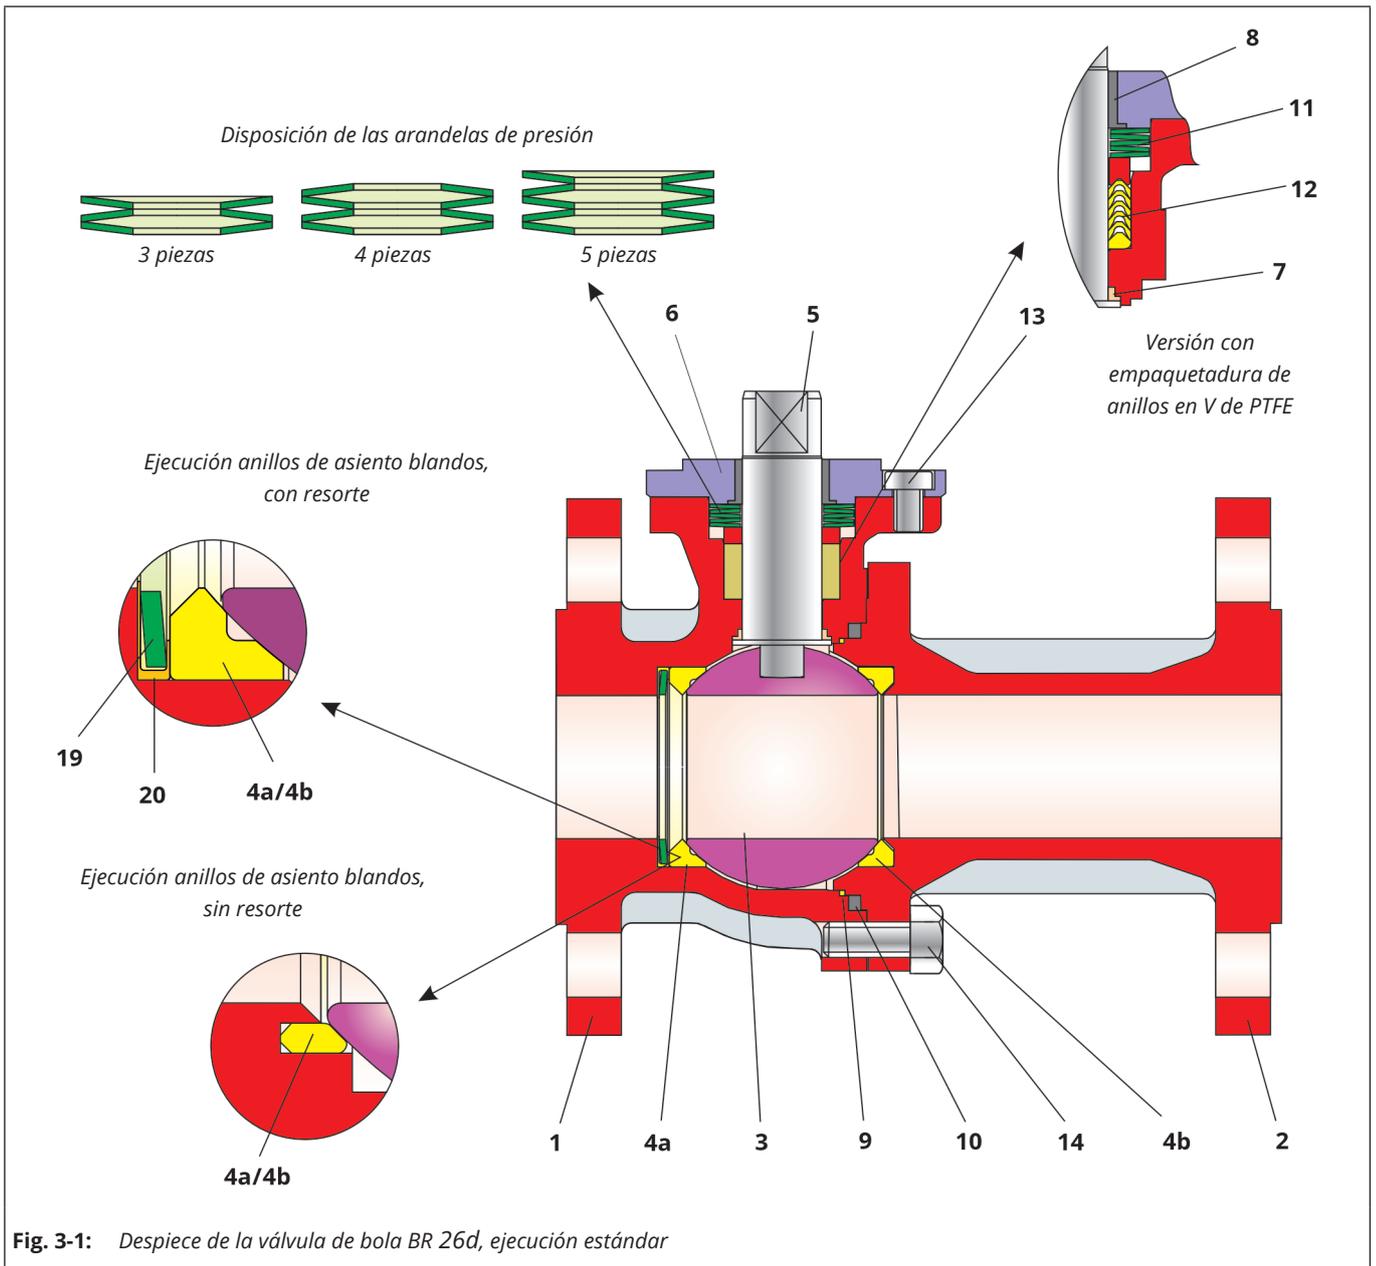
Despiece de la válvula de bola BR 26d, ejecución estándar
